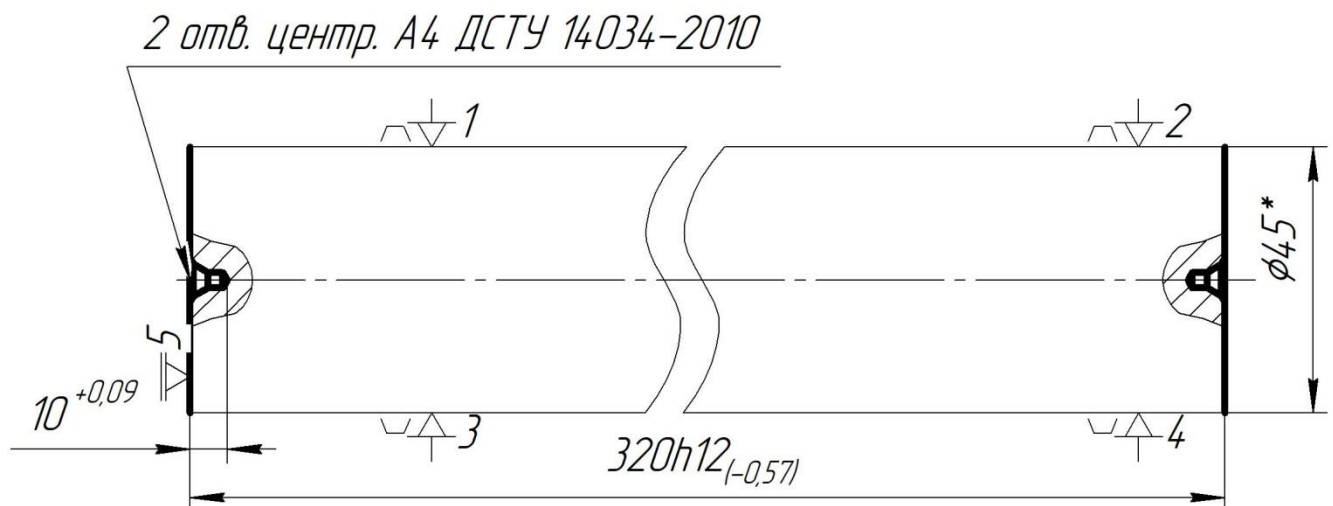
Схема установки заготовки на призми з притиском прихватами
